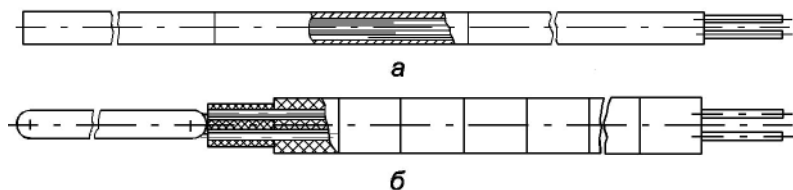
Конструкція вимірювального пакета: а — мідного; б — платинового
